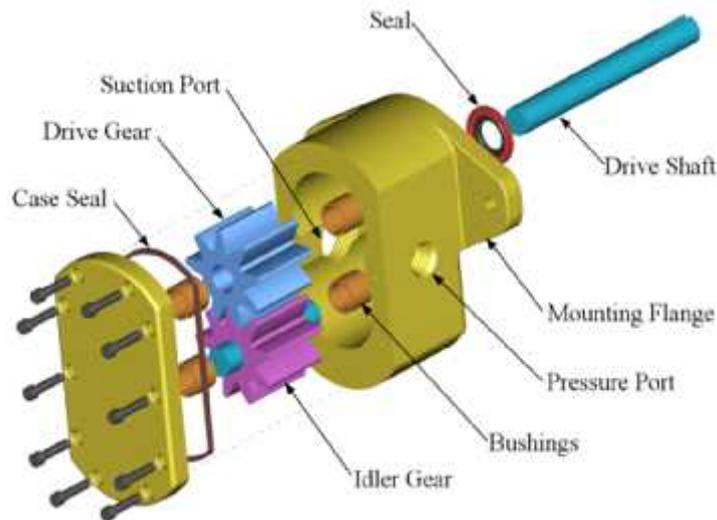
Vue éclatée d'une pompe à engrenages externes. [1]
